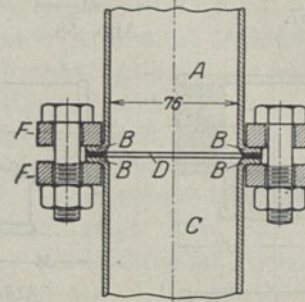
Aufgebördelte Bordringe mit Überwurfflanschen.
